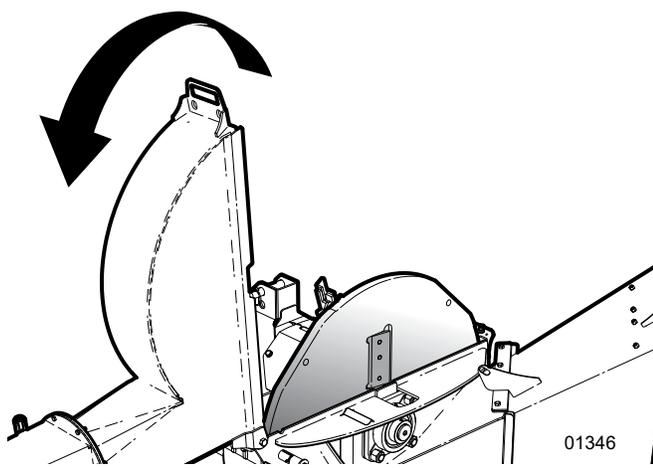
Ouvrez le boîtier supérieur du rotor
